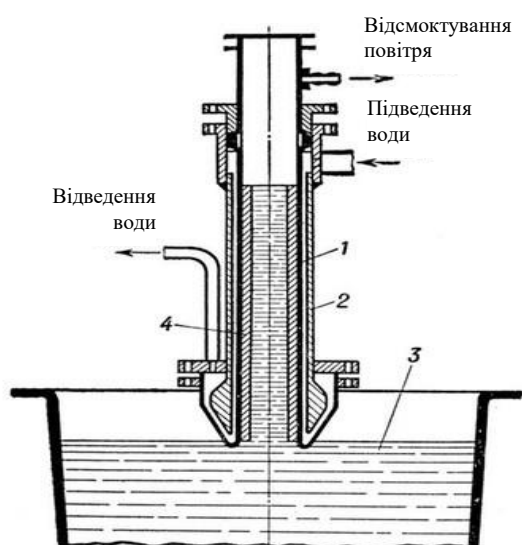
Схема ЛВВ: 1 - кристалізатор; 2 - охолоджувач; 3 - розплав; 4 - металева форма
